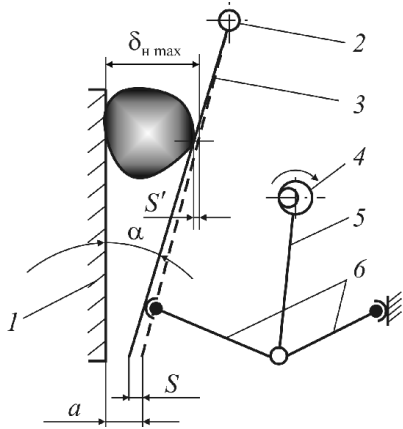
Схема щековой дробилки с простым движением щеки: 1 — неподвижная щека; 2 — ось подвеса; 3 — подвижная щека; 4 — эксцентриковый вал; 5 — шатун; 6 — распорные плиты
